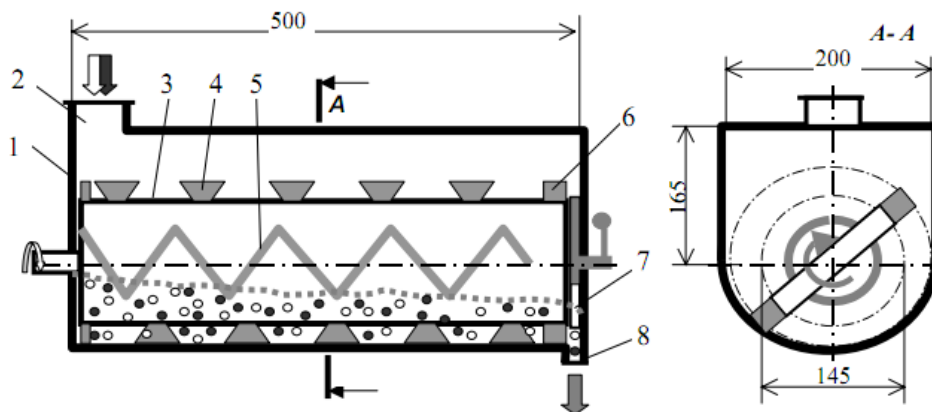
Схема и основные размеры смесителя GCM500 компании Gericke:
